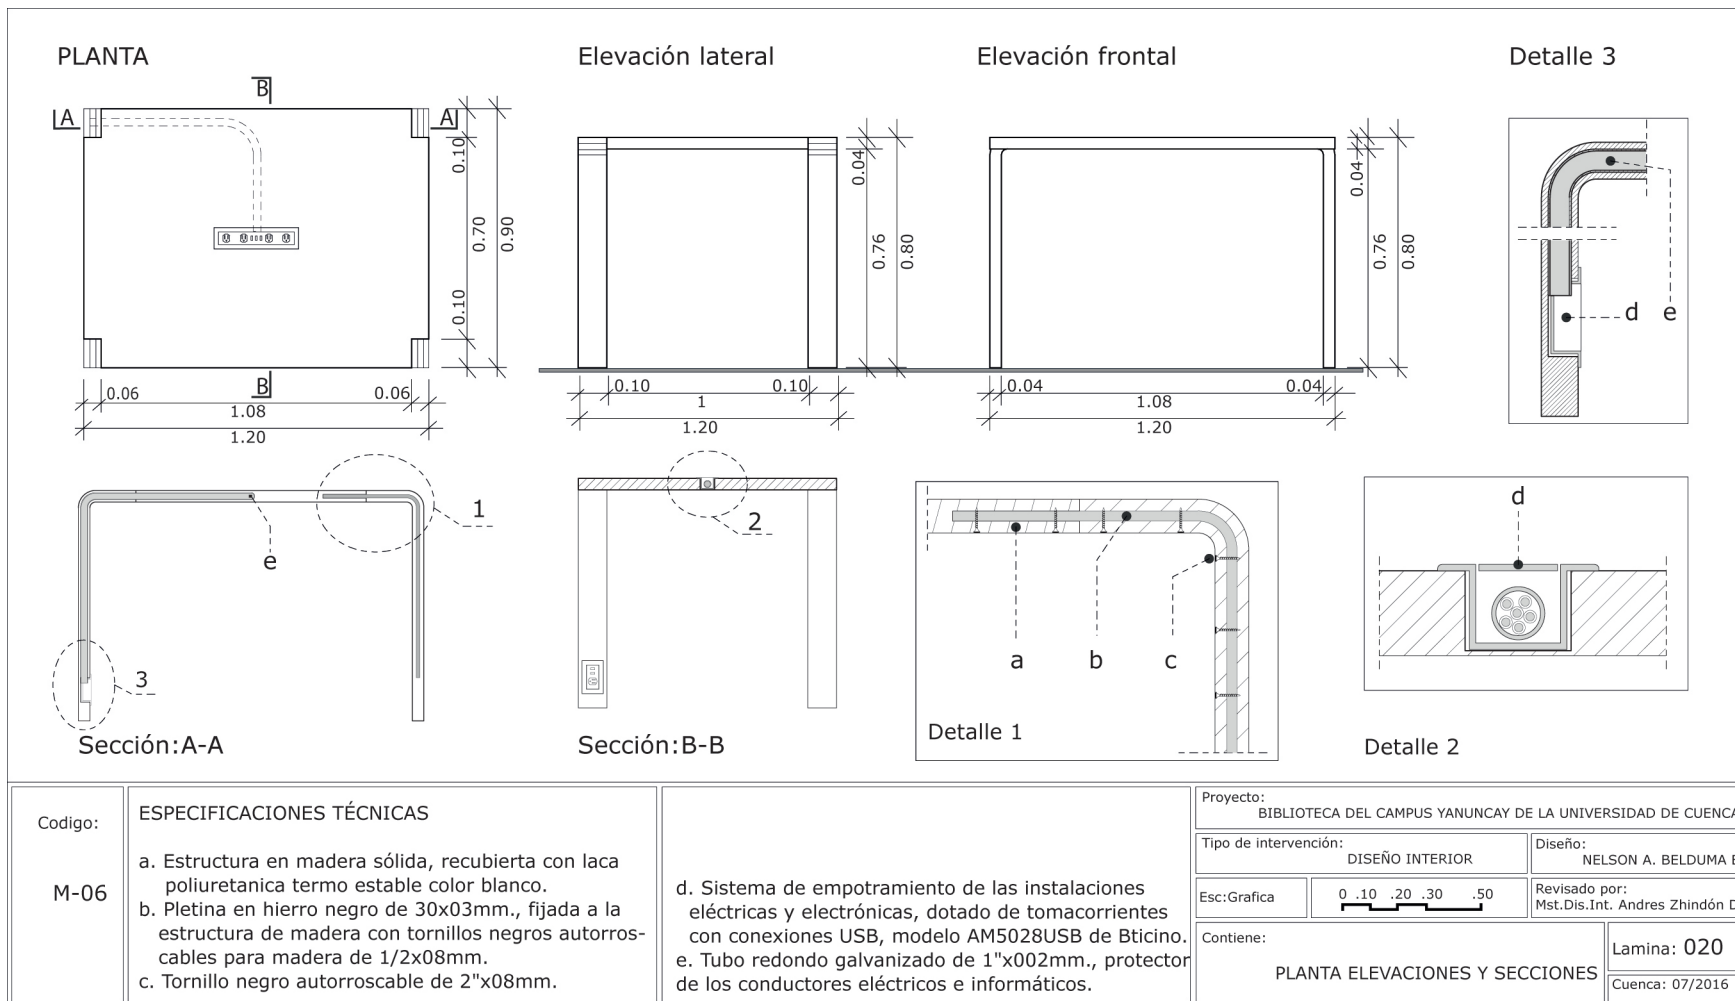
Planta, elevaciones y secciones. Mesas para trabajo en grupo. M-06.
